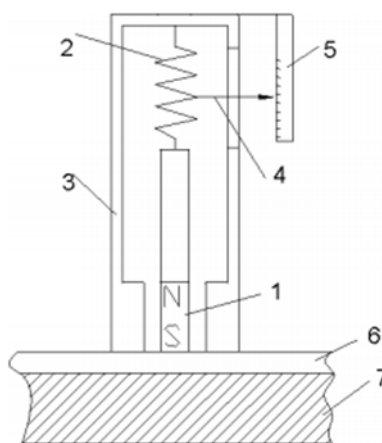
Условная схема пондеромоторного толщиномера: 1 – постоянный магнит; 2 – пружина динамометра; 3 – корпус; 4 – указатель; 5 – шкала; 6 – покрытие; 7 – ферромагнитная основа
